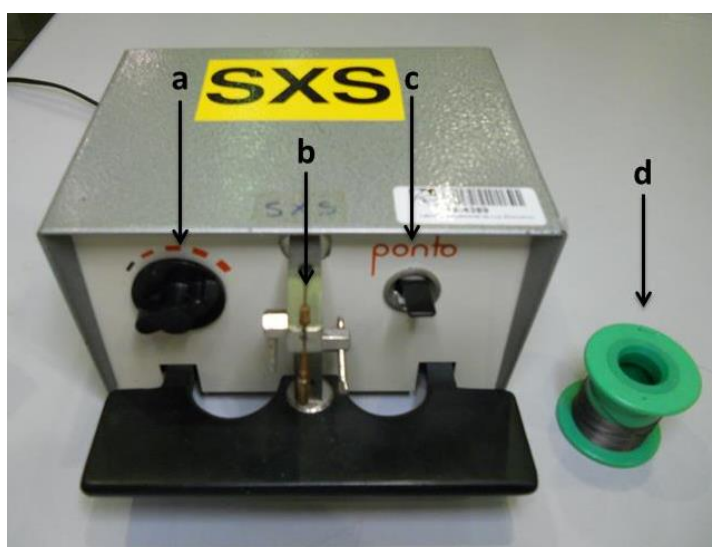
Soldador de fios de tungstênio: a) ajuste da potência; b) região de soldagem; c) botão de disparo para a solda e d) rolo com fio de tungstênio.
